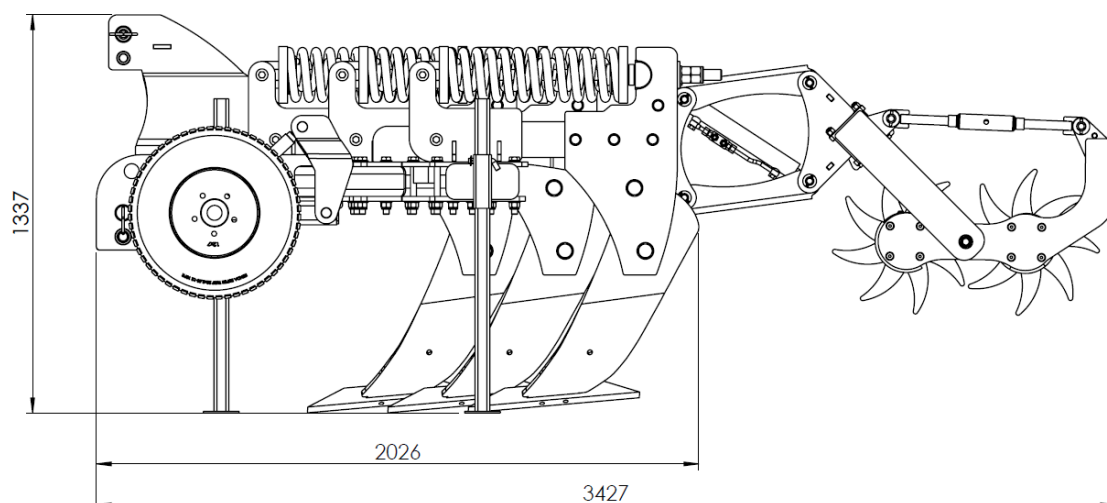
Dimensiones del subsolador - vista desde la izquierda
